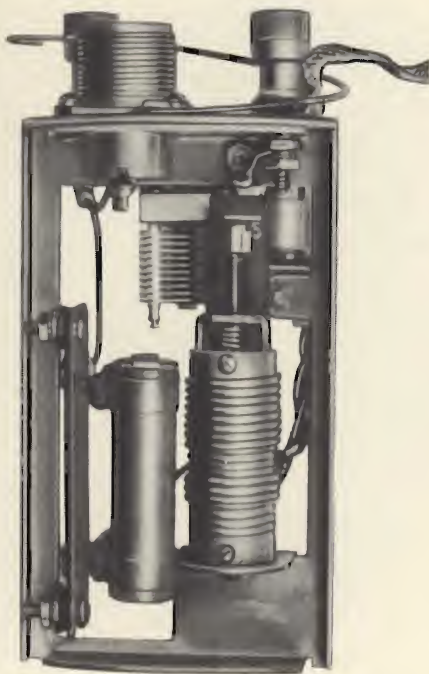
Altra vista del montaggio interno dei componenti. Si noti la praticità e la solidità del montaggio.
